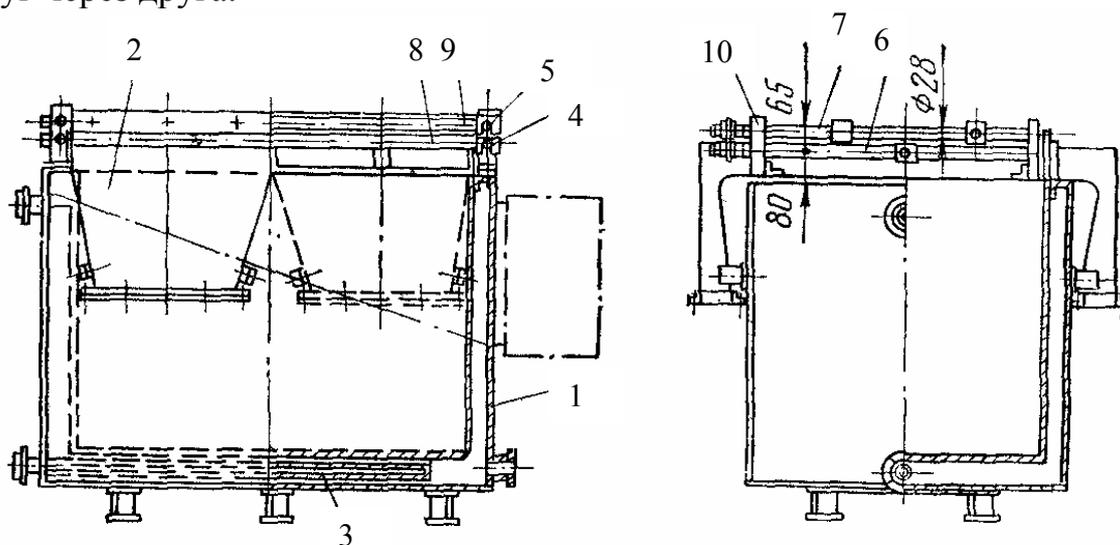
Гальваническая ванна: 1 – корпус; 2 – бортовой отсос; 3 – труба для подвода сжатого воздуха; 4 и 5 – катодный и анодный кабели; 6 и 7 – катодная и анодная неподвижные штанги; 8 и 9 – катодная и анодная подвижные штанги; 10 – изолятор под штанги
